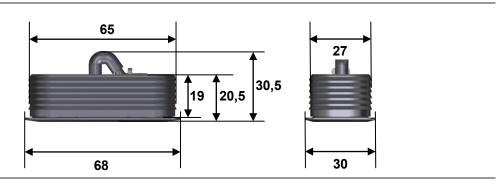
Bedienelement TOUCHbasic-inlay, Montagemaße (Angaben in mm)
